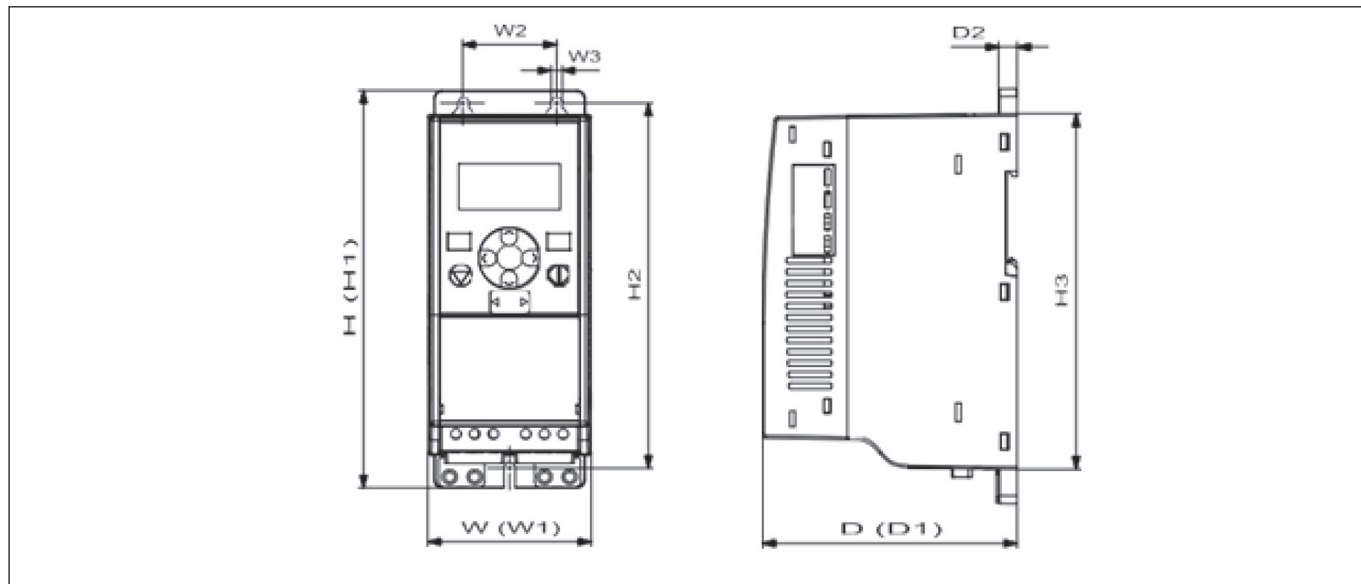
Размеры преобразователя VACON® 10, MI1 — MI3
